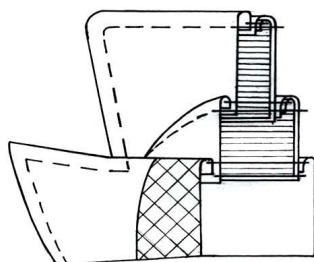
Сборочная схема обработки воротников в изделиях из тонкой кожи
